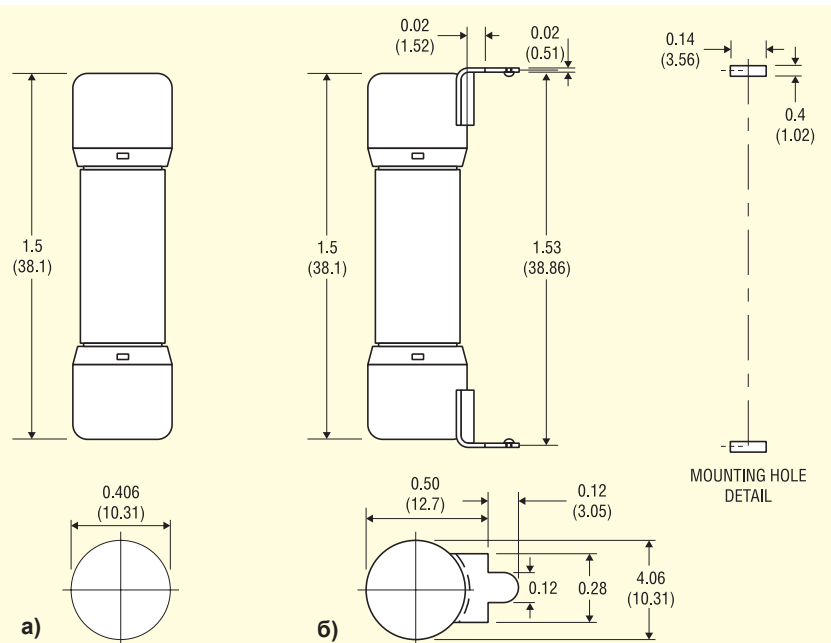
Корпуси, у яких виготовляються запобіжники серії KLKD: версія Ferrule (а); версія PCB (б). розміри вказано в дюймах, а в дужках — у міліметрах
